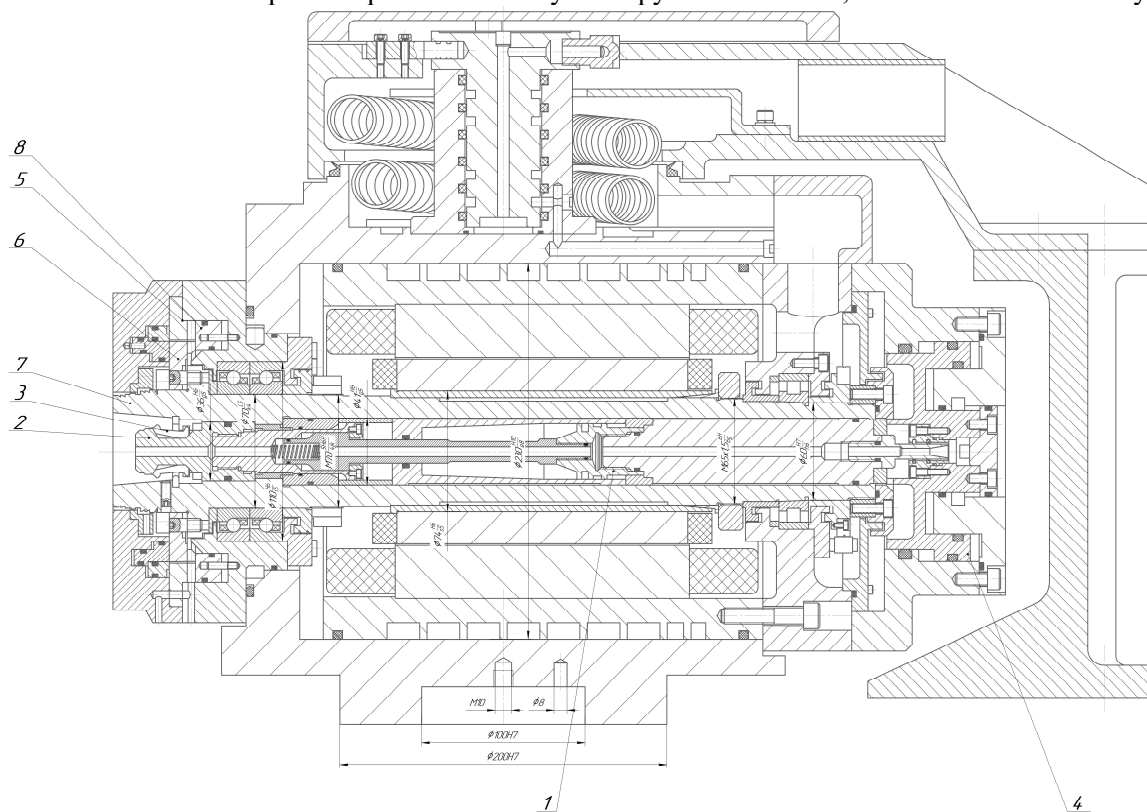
Фрезерний шпиндель верстата Puma MX2100ST
